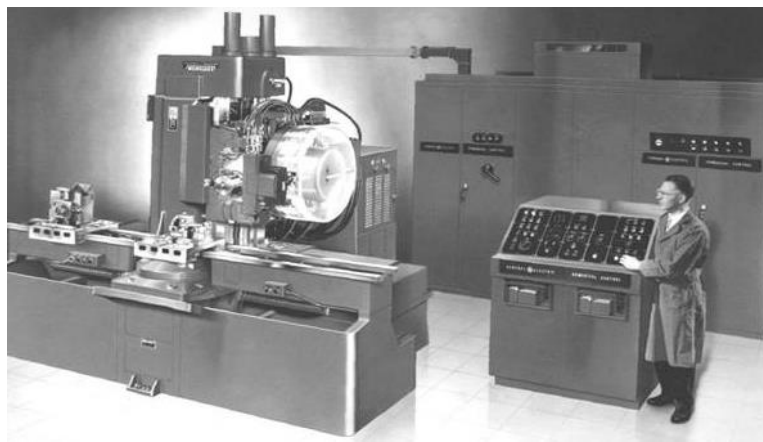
Máquina-herramienta CN presentada en el Machine Tools Show, Chicago, 1955 [39].
